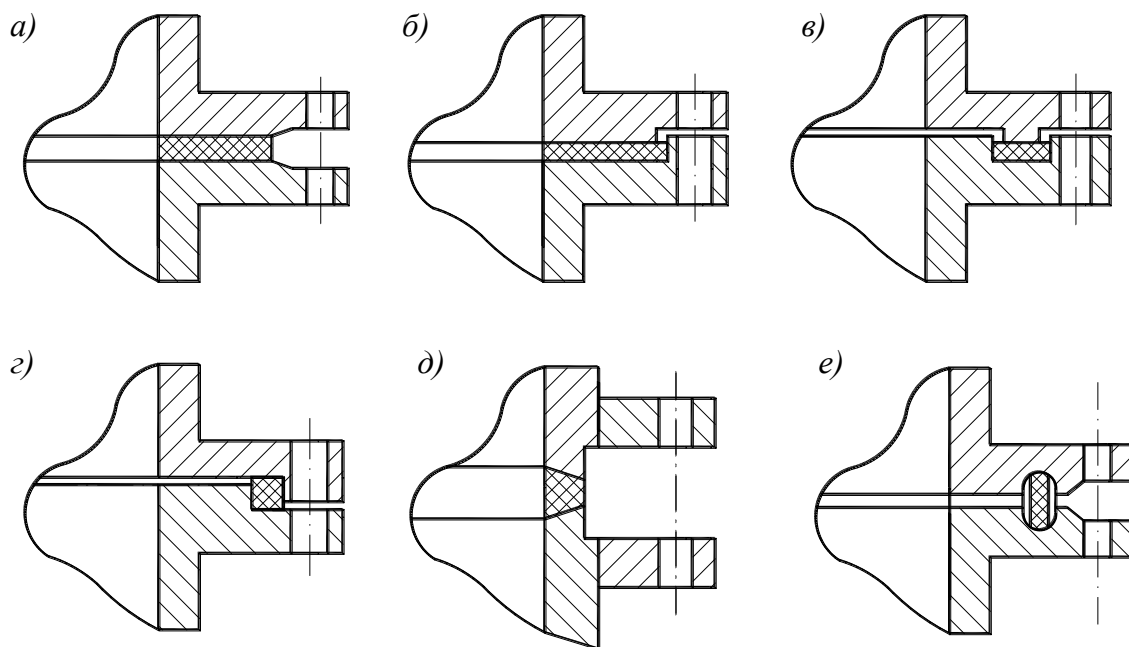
Типы уплотнительных поверхностей фланцевых соединений:
